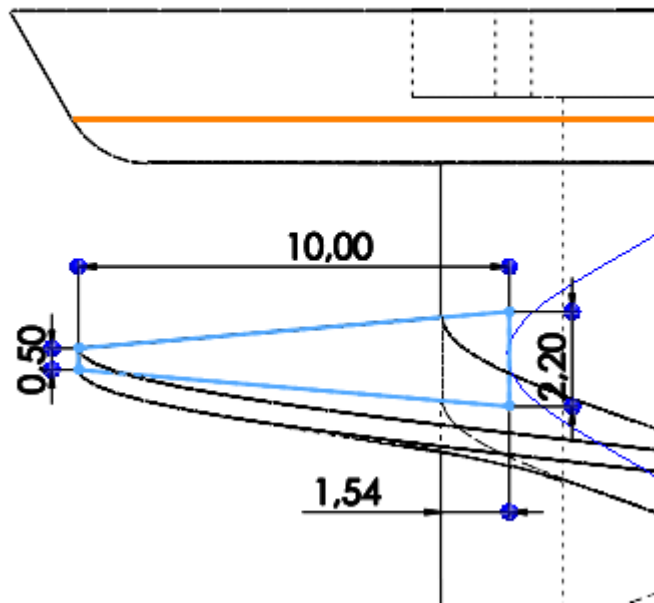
Поперечний переріз витка різі у деталі «Гвинт»
